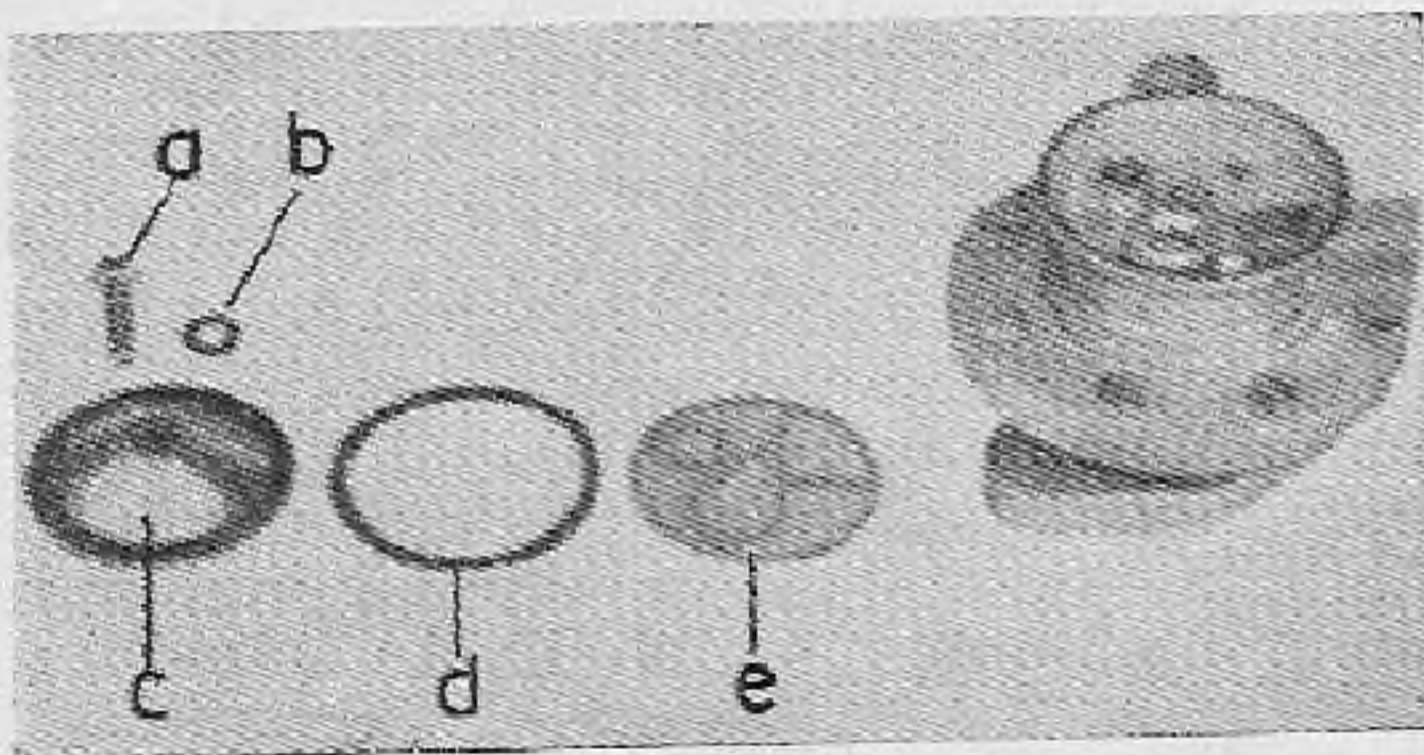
Componentes de la tapa superior de la bomba de combustible.
